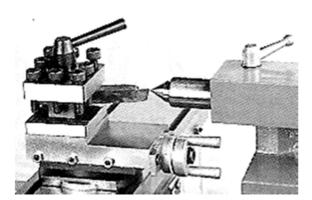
Einrichten der Bearbeitungswerkzeuge
